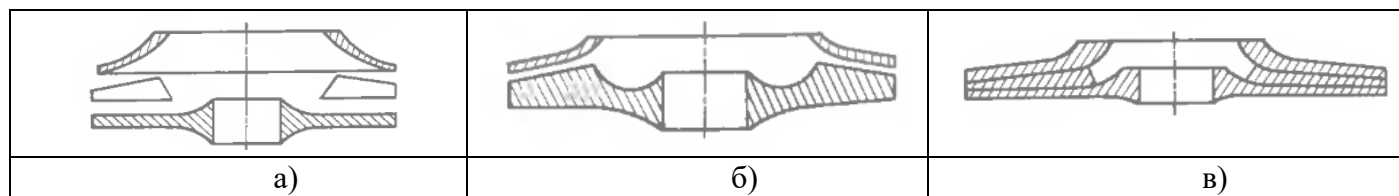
Конструкции рабочих колес: а — открытая; б — полуоткрытая; в — закрытая
